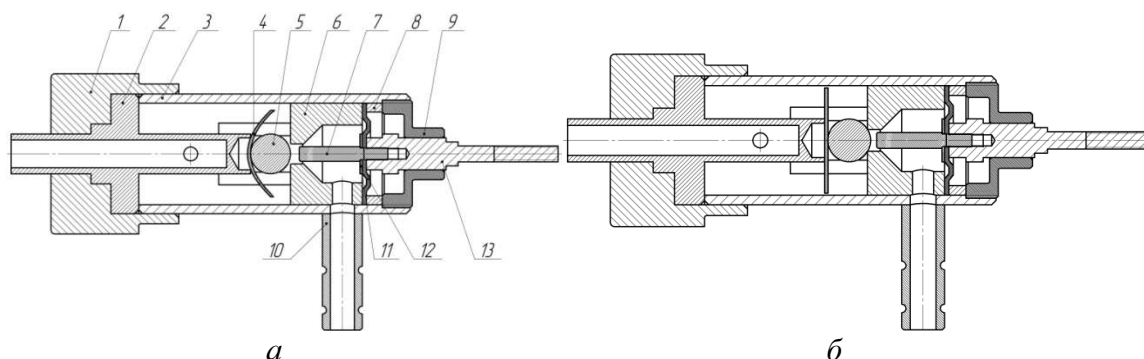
Автоматический термозапорный клапан: а) положение «открыто»; б) положение «закрыто»; 1 – винтовая крышка; 2 – втулка; 3 – корпус; 4 – TiNi элемент; 5 – шарик; 6 – перепускная втулка; 7 – винт; 8 – кольцо; 9 – крышка; 10 – ниппель; 11 – кольцо; 12 – ниппель; 13 – шток
